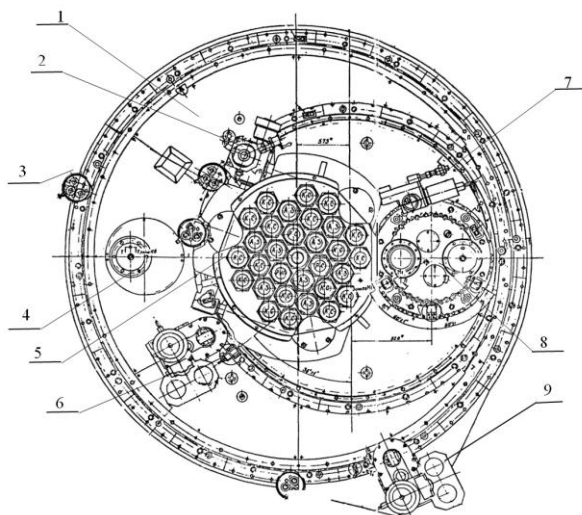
Пробки поворотные с приводами (вид в плане): 1 – пробка большая поворотная, 2 – привод подъема направляющих труб, 3 – блок датчиков, 4 – пробка люка-лаза, 5 – колонна СУЗ, 6 – привод колонны СУЗ, 7 – привод малой поворотной пробки, 8 – малая поворотная пробка, 9 – привод большой поворотной пробки
